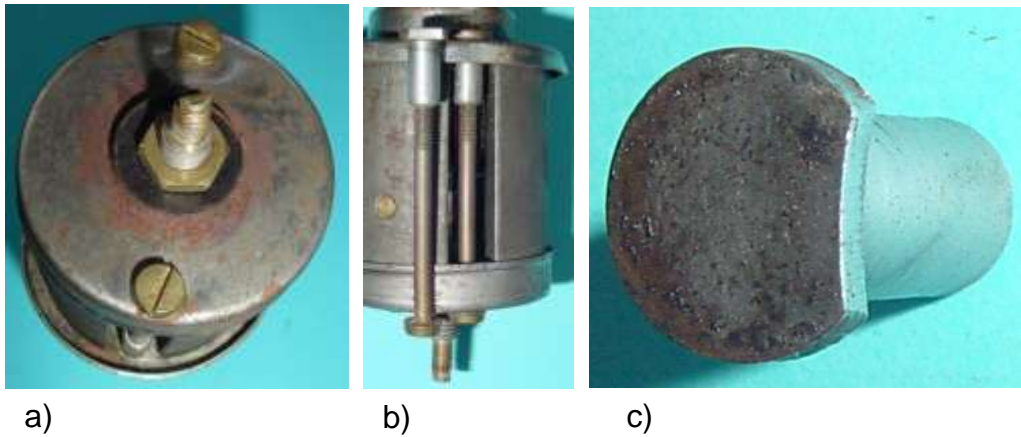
Befestigung des Lagerhalses am Erregersystem: a) Bolzenköpfe am Boden, b) Bolzen mit Gewindehülse, c) Einseitig verschlossene Gewindehülse
